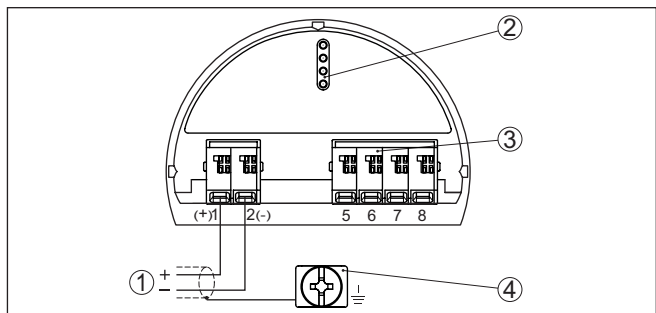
Bedienings- en aansluitruimte (Ex ia) bij instrumenten met intrinsiekveilige stroomuitgang
